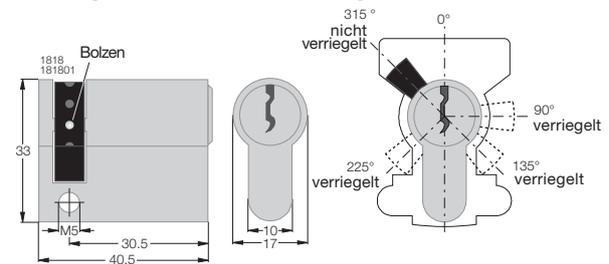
Schließzylinder [Best.-Nr. 1818, 1818 01]
